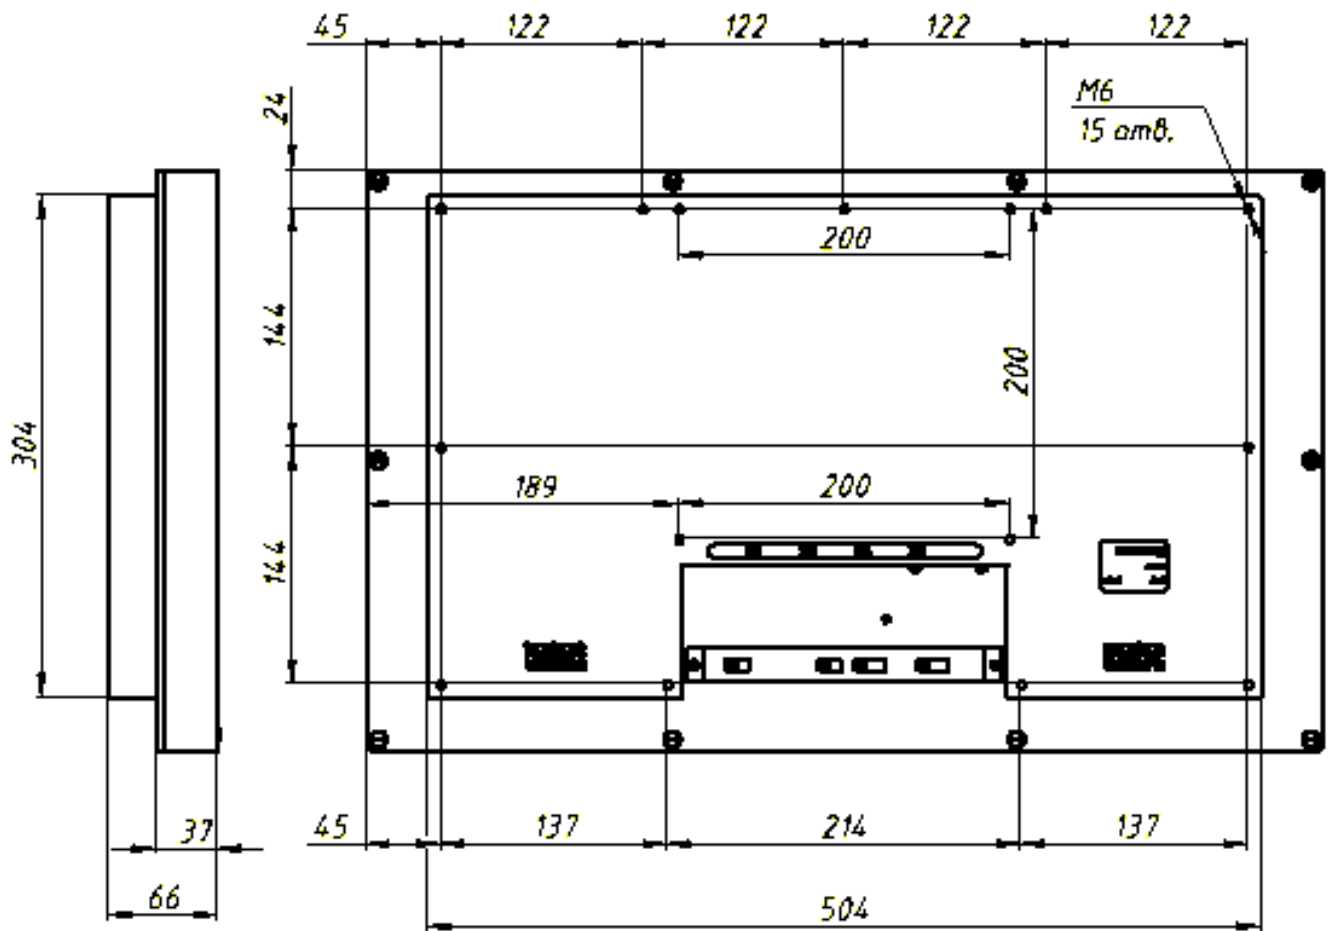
д – Габаритный чертёж видеомонитора в исполнении ВМП1225-АД-5-Х-Х-Х, вид сбоку и сзади, положения отверстий для крепления в щите и крепления VESA
